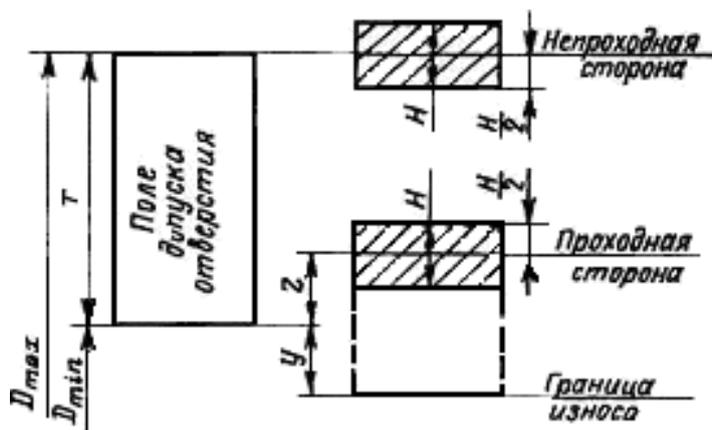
Схема расположения полей допусков калибров для отверстий
